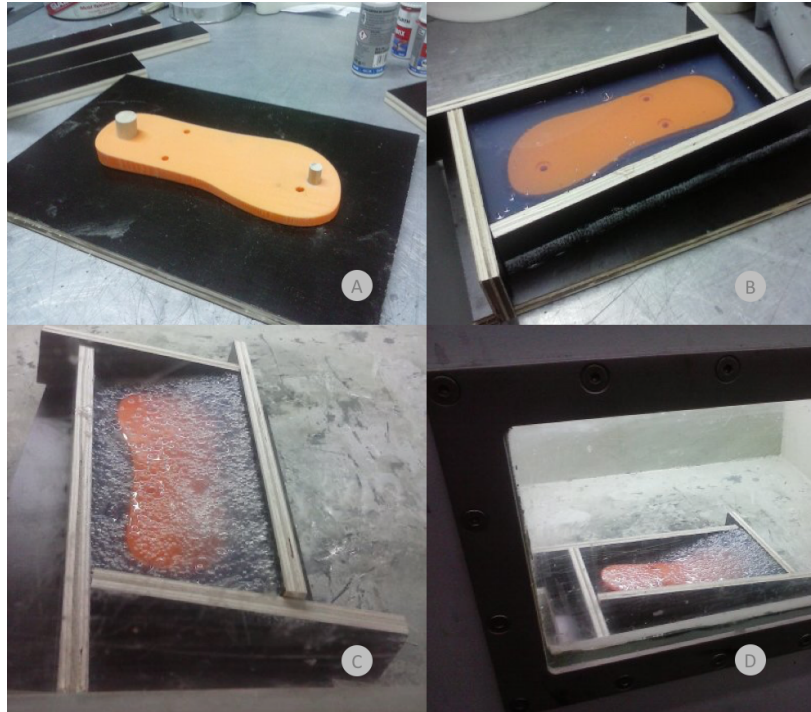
A) Peça 3D; B) Vazamento do silicone; C e D) Camara de vácuo com molde inclinado.
